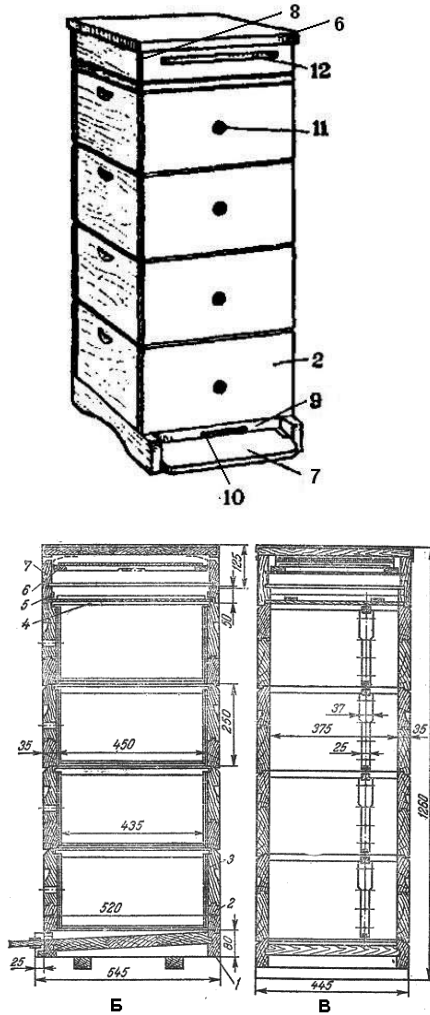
Многокорпусный улей: А – общий вид; Б – продольный разрез; В – поперечный разрез; 1 – дно; 2 – корпус; 3 – рамка; 4 – потолок; 5 – подкрышник; 6 – вентиляционная рама; 7 – кровля; 8 – обвязка крыши; 9 – прилетная доска; 10 – летковый вкладыш; 11 – верхний леток; 12 – пропил для вентиляции.
